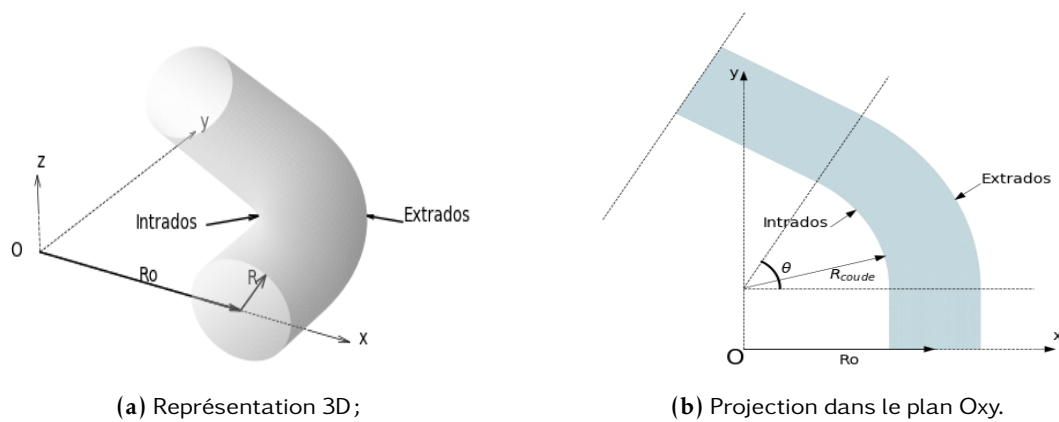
Paramètres utilisés pour définir un tube coudé.
